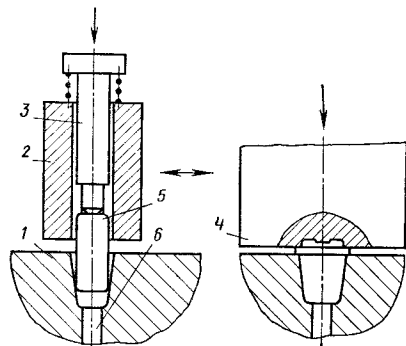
Схемы штамповки заготовок конических и цилиндрических роликов
